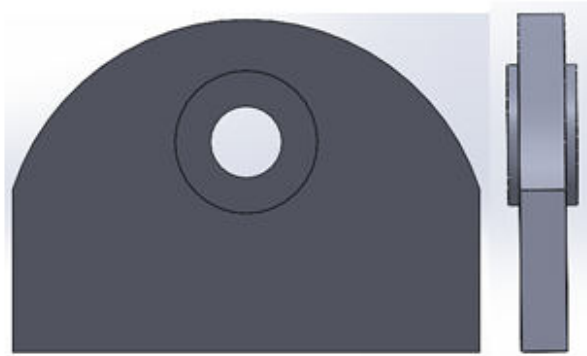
Alzado y perfil del refuerzo aplicado en la orejeta.
